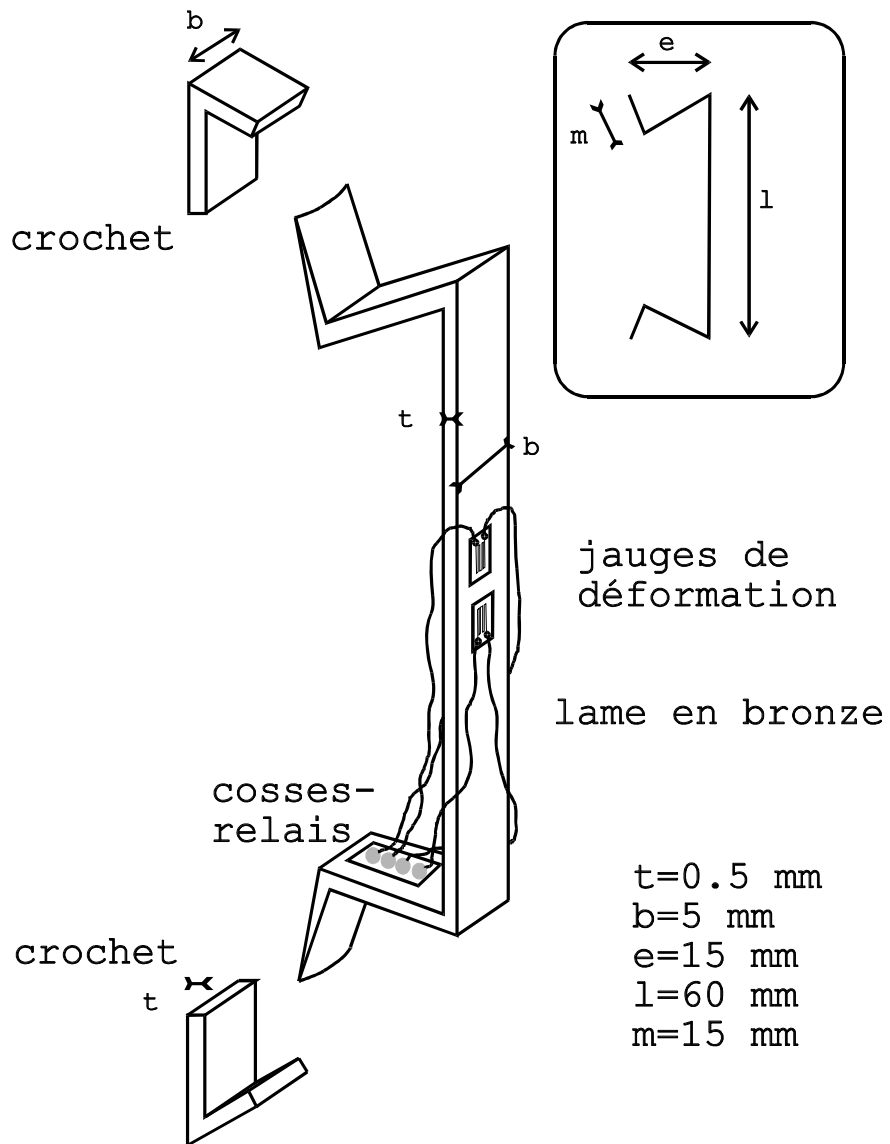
Capteur interne de déformation axiale : schéma de forme et dimensions
